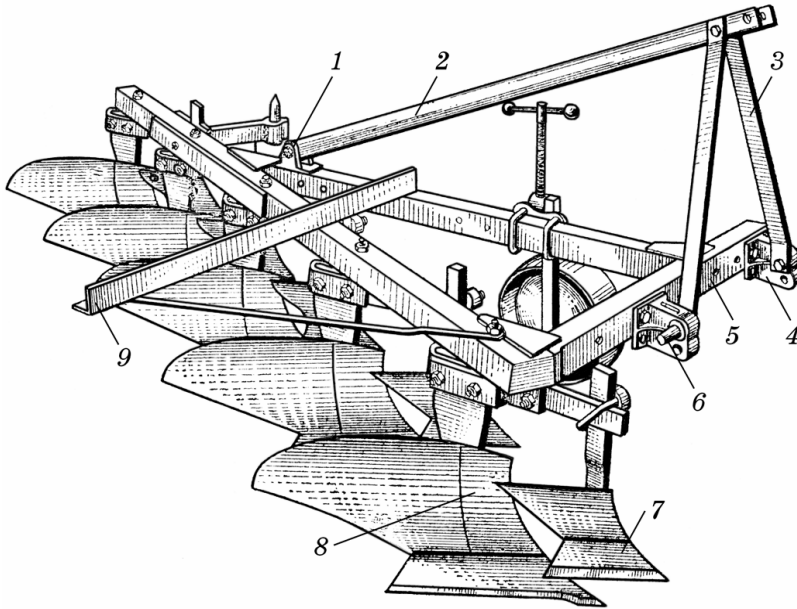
Плуг п'ятикорпусний начіпний ПЛН-5-35:
